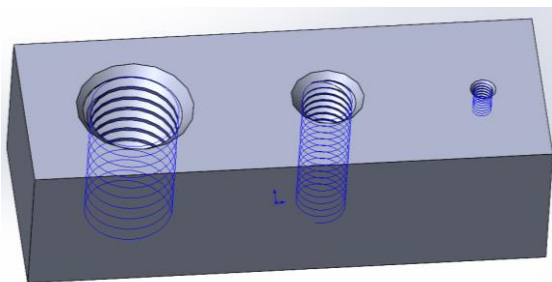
3D-модель образца с внутренними резьбами M3, M8 и M14, выполненная в САПР SolidWorks
